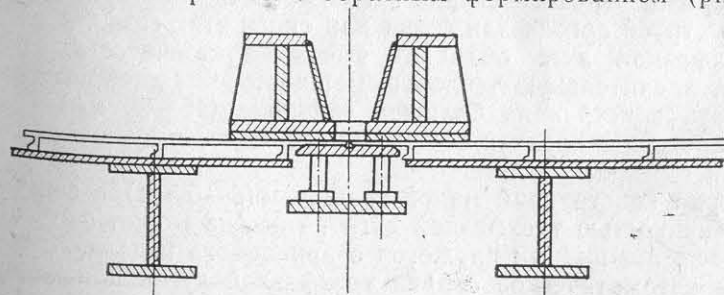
Схема установки прессованных панелей на стенде под автоматическую сварку.
